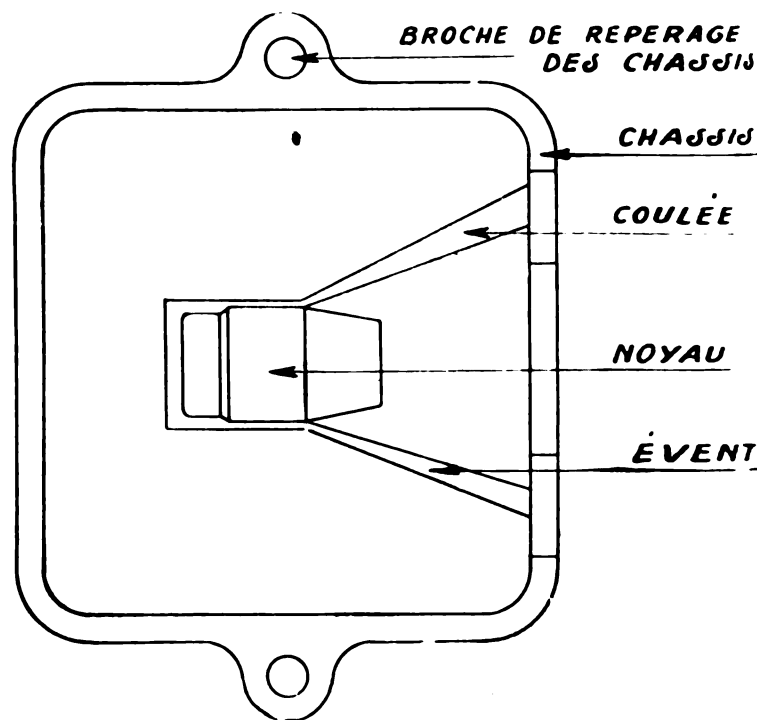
Le moulage. Noyau en place avant de remettre le demi-moule supérieur
